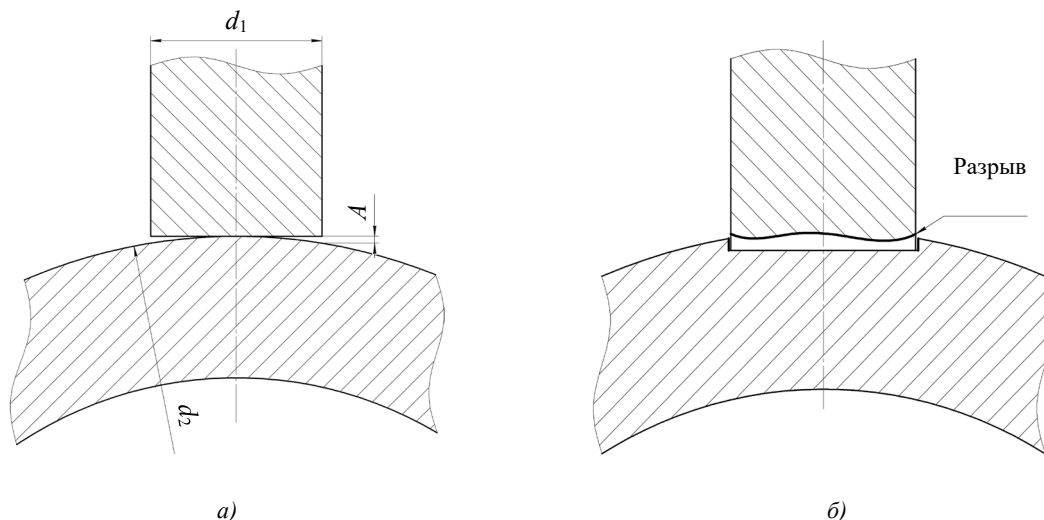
Имитаторы штуцерного узла: а — имитатор таврового соединения; б — соединение с предварительной выточкой канавки; d_1 — диаметр имитатора штуцера; d_2 — диаметр имитатора корпуса; A — зазор
